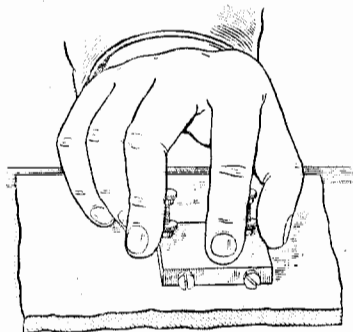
Приспособление с винтами на зеркальном стекле.
